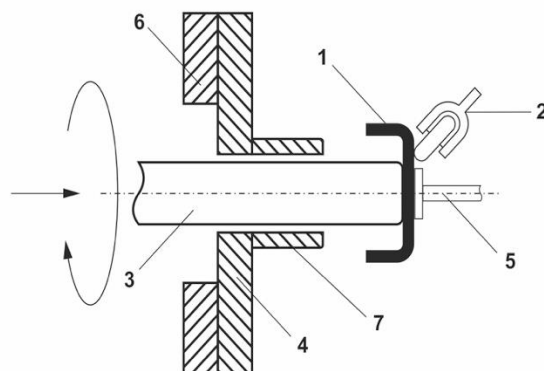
Схема формообразования полой листовой детали методом обкатки с автоматической подачей оправки на станке с ЧПУ при помощи дополнительной технологической оправки:
